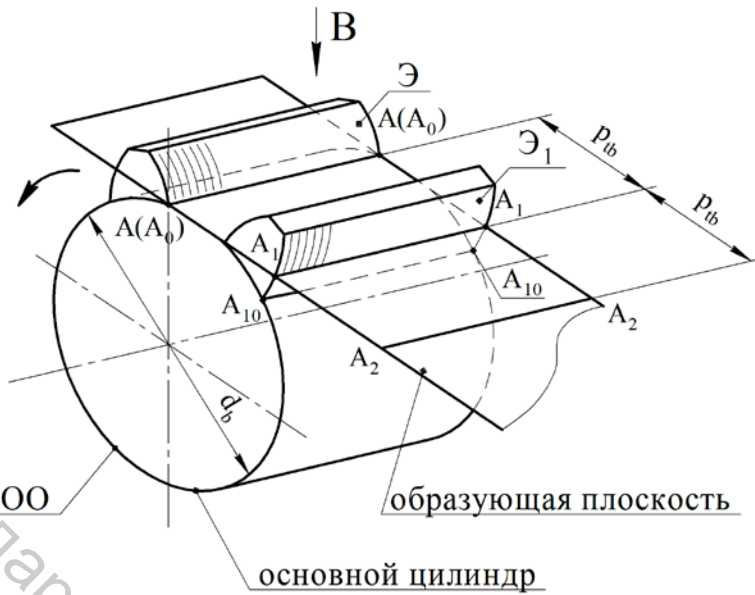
Образование рабочих поверхностей прямых зубьев цилиндрического колеса
